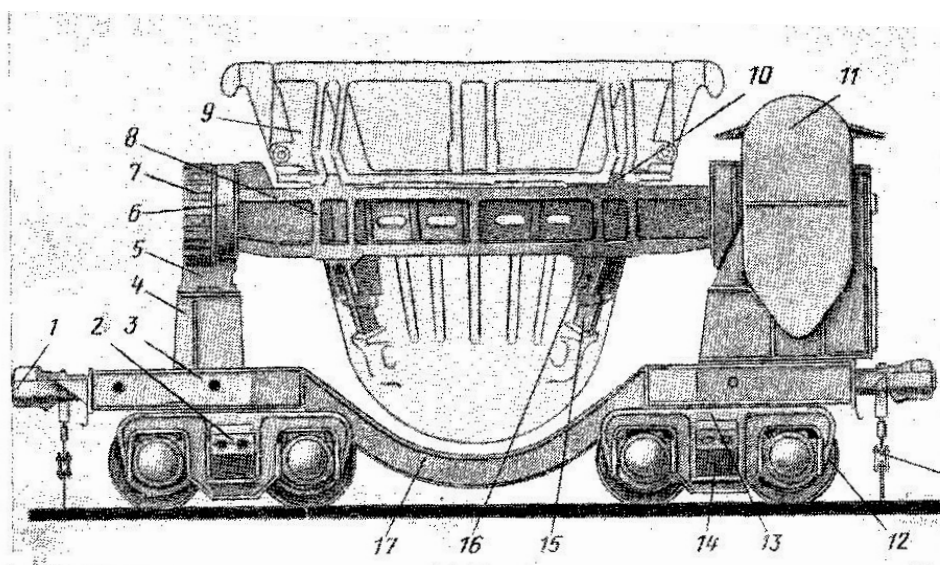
Несамohодный шлаковоз: 1 — автосцепка; 2 — балка; 3 — лафет; 4 — стойка рамы; 5 — направляющие; 6 — каток; 7 — зубчатый сектор; 8 — опорное кольцо; 9 — шлаковый ковш; 10 — выступ; 11 — кожух; 12 — колесная пара; 13 — продольная балка; 14 — рессоры; 15 — рычаги; 16 — кронштейн; 17 — балка
